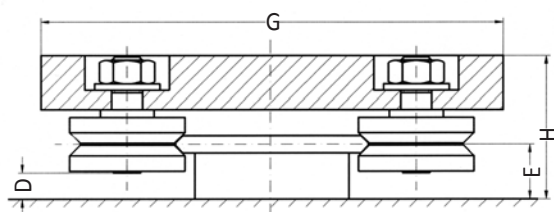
Zusammenbau 90° System | Fig.3: Assembly 90° system
